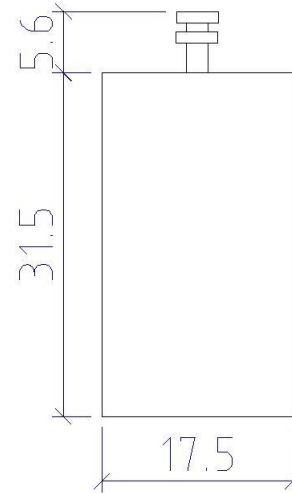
Pemasangan Bilah Pisau dengan Besi Plat Las bagian tengah bilah pisau dengan besi poros
